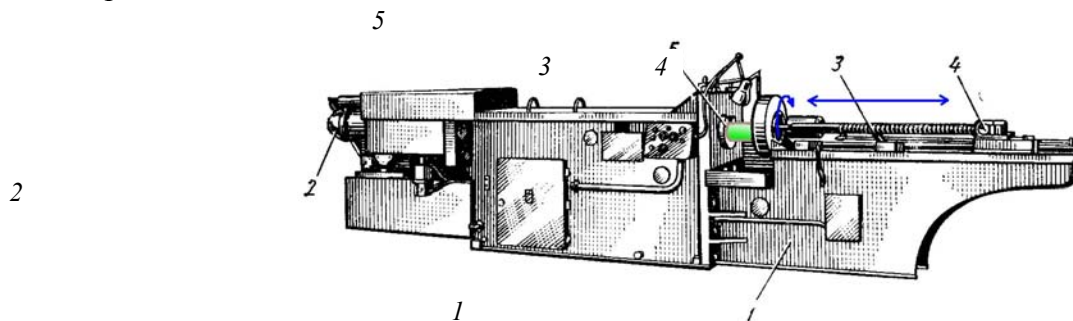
Горизонтально-протяжный станок 7Б55:
